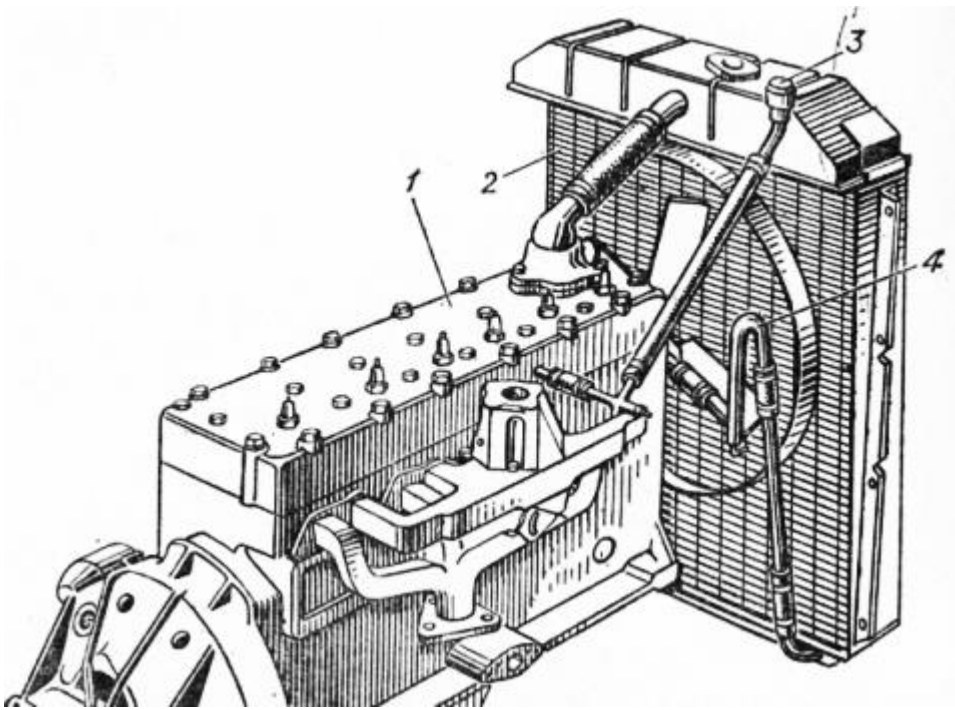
Схема оборудования двигателя для разогрева его горячей водой (способ НИИА): 1— двигатель; 2 — радиатор; 3 — заливная Еоронка; 4 — повышающая петля
